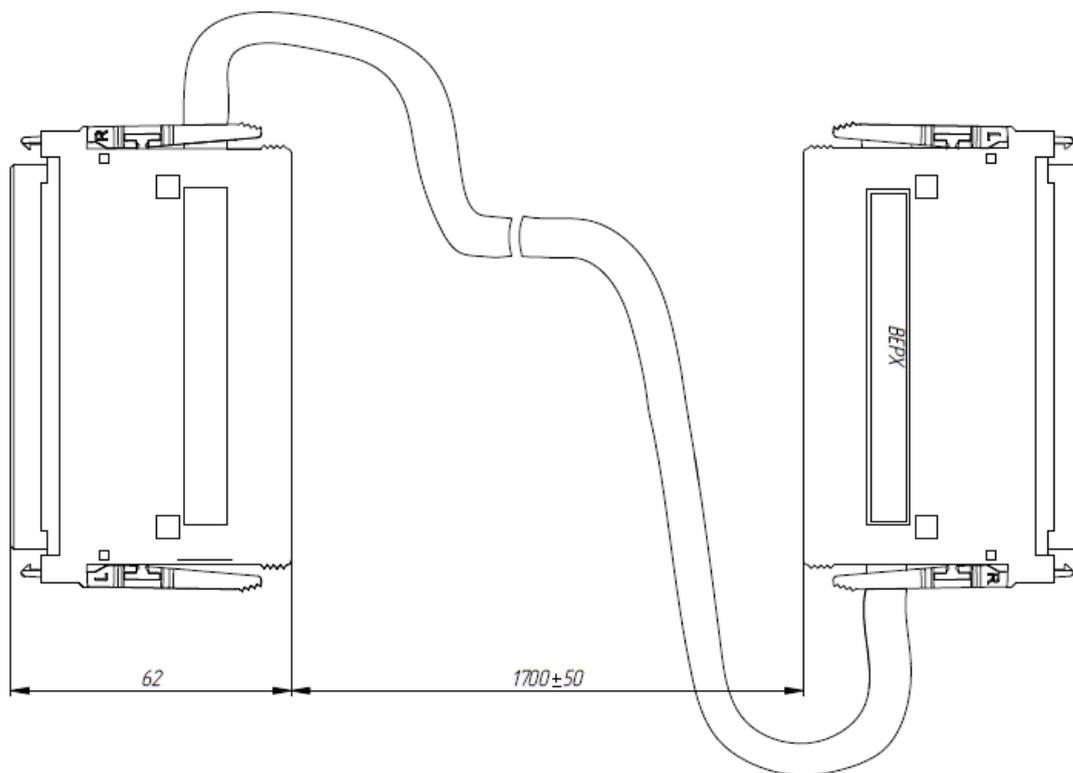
Внешний вид и габаритные размеры кабеля модуля резервирования
